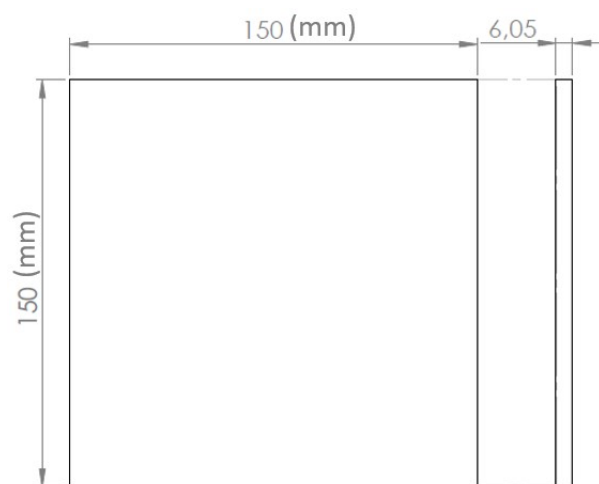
Dimensões do  $CP_{CHAPA}$  fabricado com aço INOX em milímetro.
